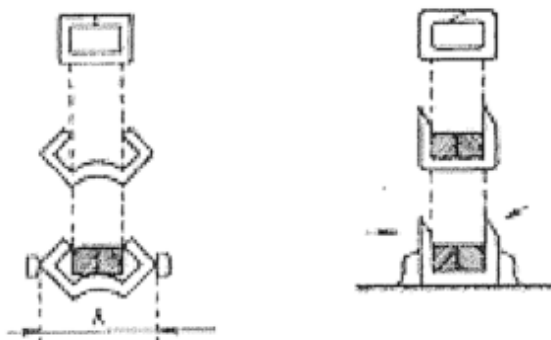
Соединения заготовок обоймами (A – раствор клещей)
